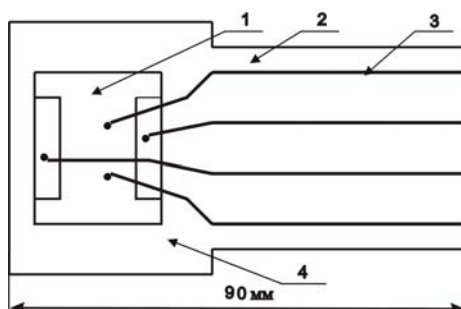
Конструкция пленочного арсенид галлиевого датчика Холла ХА1-П: 1 - эпитаксиальная структура; 2 - гибкая печатная плата на основе полиимидно-фторопластовой композиции; 3-проводники; 4 - металлический немагнитный корпус
